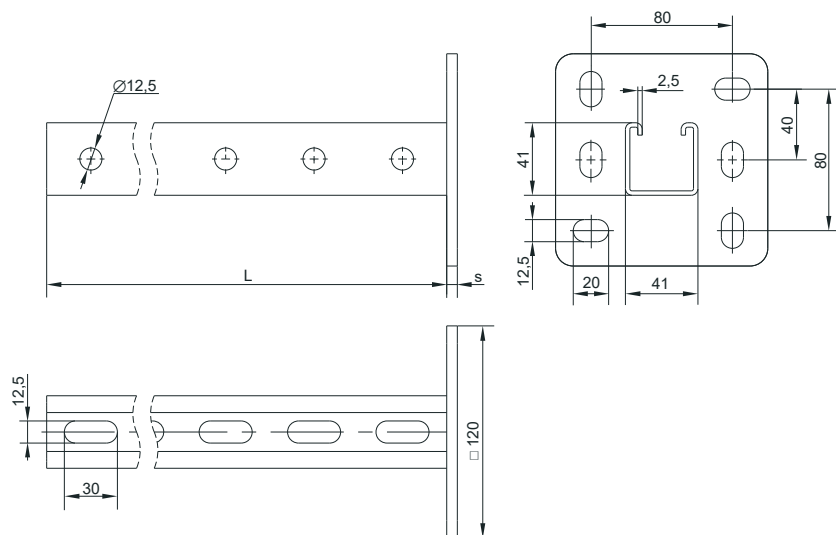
Подвес потолочный 41x41 / Figure B.2 – Ceiling suspension 41x41
